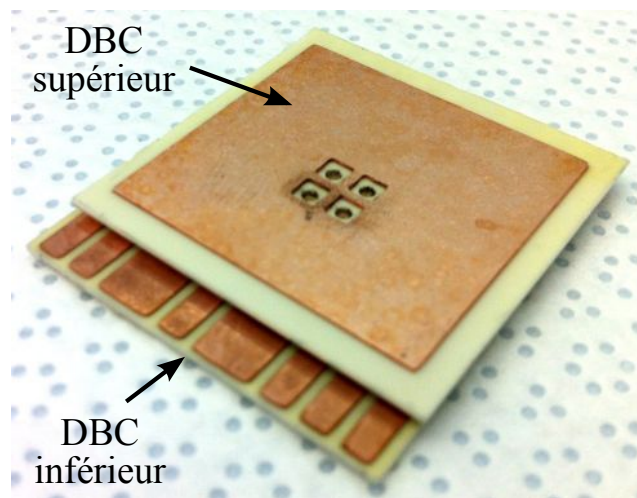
Photo d'un ensemble assemblé par le four RTA
